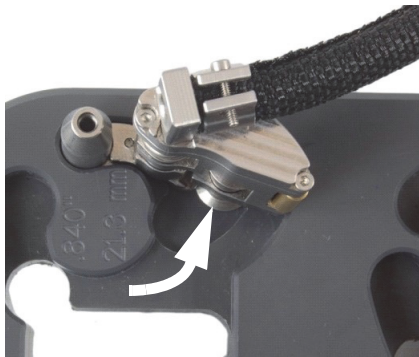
Introducción del flanco posterior en el molde de la plantilla de configuración
